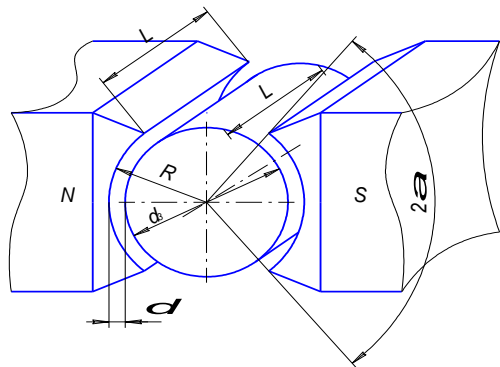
Форма рабочего зазора при MAO цилиндрических поверхностей
